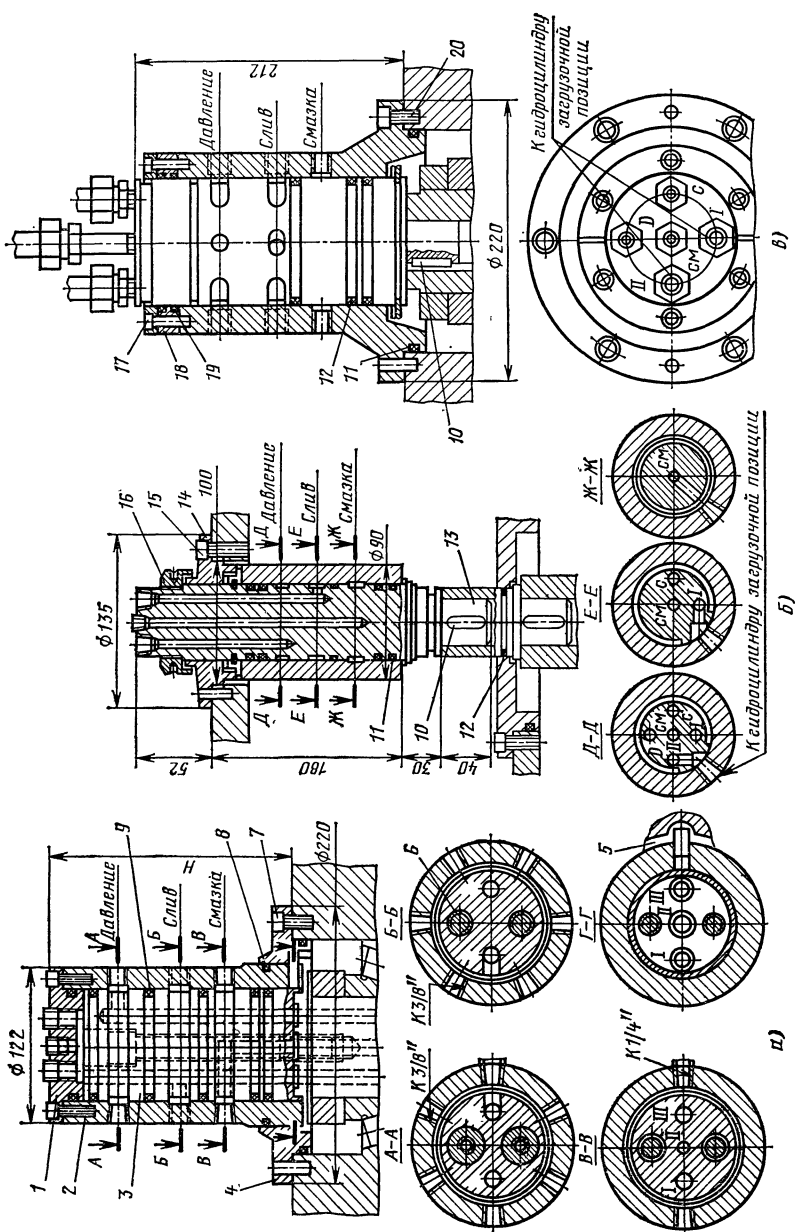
Установка маслораспределителей центрального гидропривода приспособлений:
